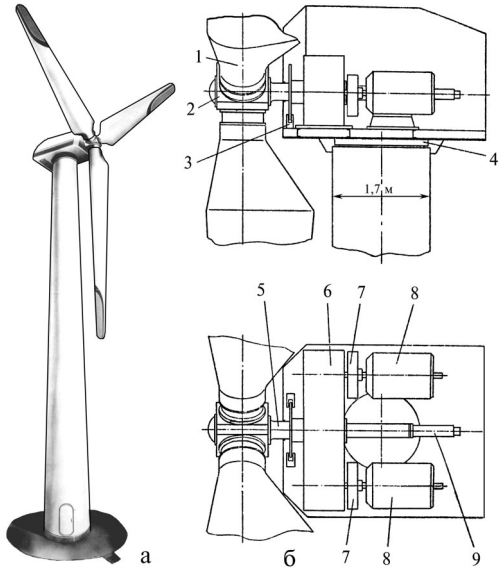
Агрегат вітроелектричний АВЕ-500: а - загальний вигляд; б - вміст головки агрегату: 1 - лопать; 2 - ступиця; 3 - гальмо вітроколеса; 4 - поворотний круг; 5 - вал; 6 - редуктор; 7 - гальмівний пристрій; 8 - генератор; 9 - пристрій повертання лопатей.
